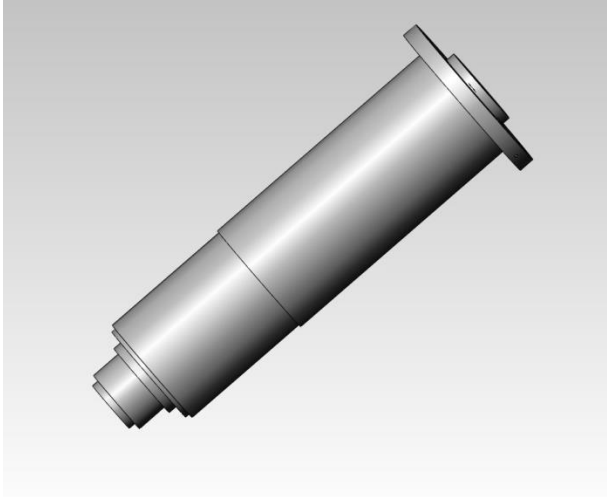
Yorulma test makinesinin kroki tasarımı
